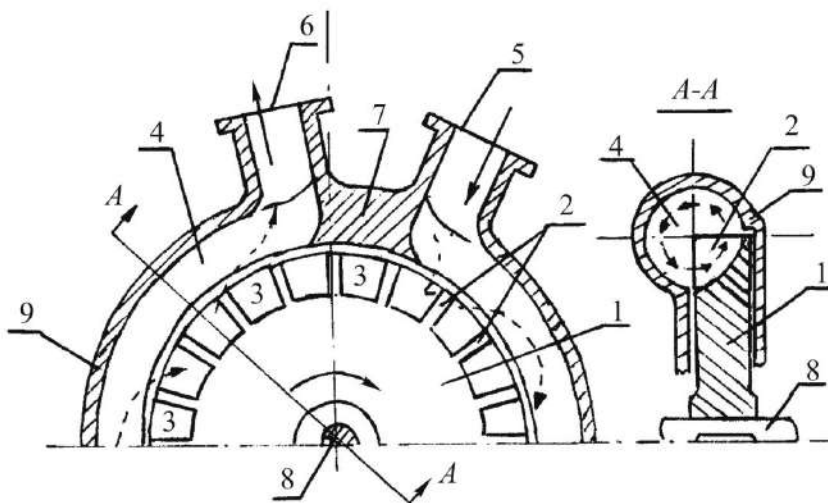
Вихревой насос: 1 – рабочее колесо; 2 – радиальные лопатки; 3 – межлопаточное пространство; 4 – кольцевой канал; 5, 6 – всасывающий и нагнетательный патрубки; 7 – разделитель потоков; 8 – вал рабочего колеса; 9 – корпус.
